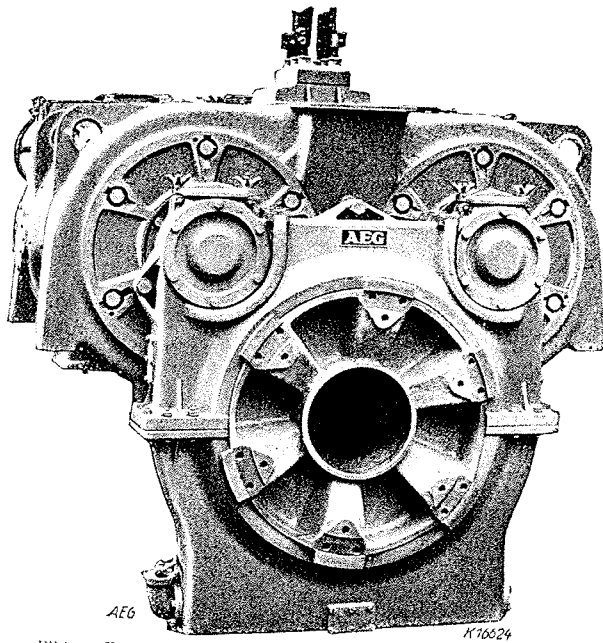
Doppelmotor mit Vorgelege und Zahnradschutzkasten.
